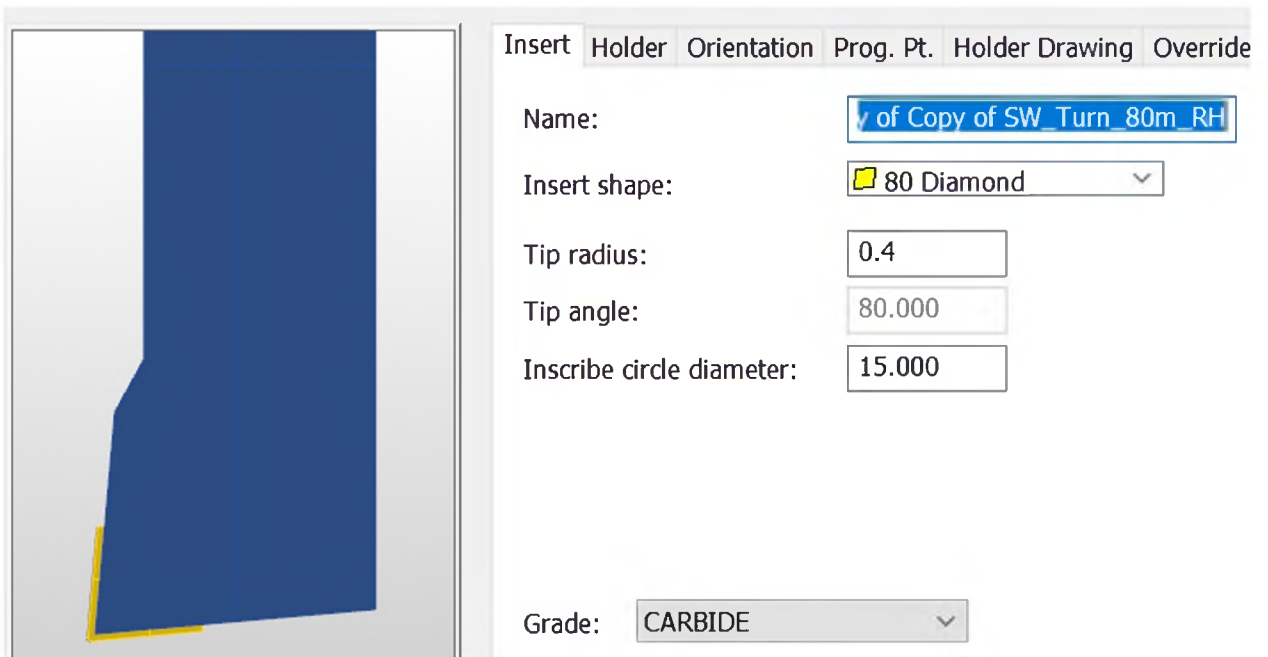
Інструмент для обробки зовнішньої поверхні
